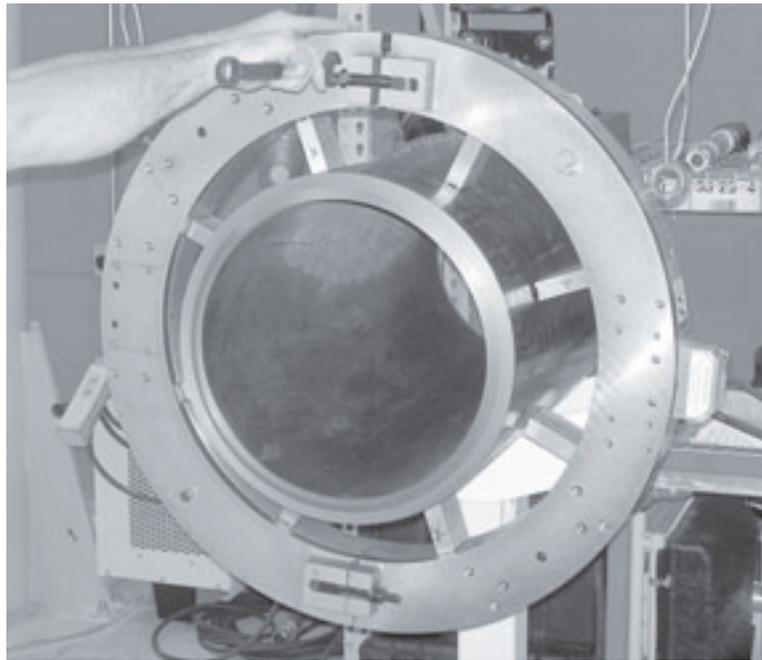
Montare le due metà della macchina intorno al tubo.
